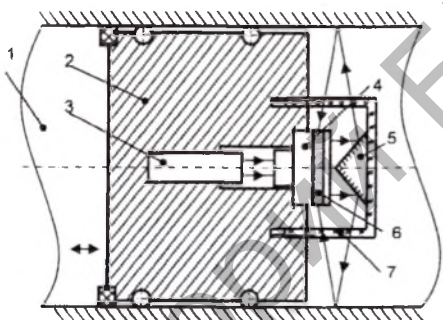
Принципиальная схема опико-механического устройства для контроля: 1 - контролируемая поверхность, 2 - перемещаемый модуль, 3 - лазер, 4 - телескоп, 5 - коническое зеркало, 6 - кольцевая ПЗС-матрица, 7 - стеклянный стакан
